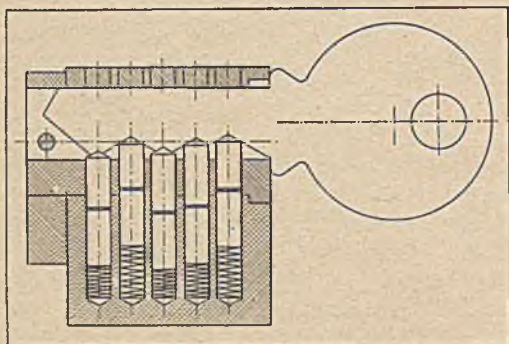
Schloßquerschnitt mit eingeführtem Falsch-Schlüssel
